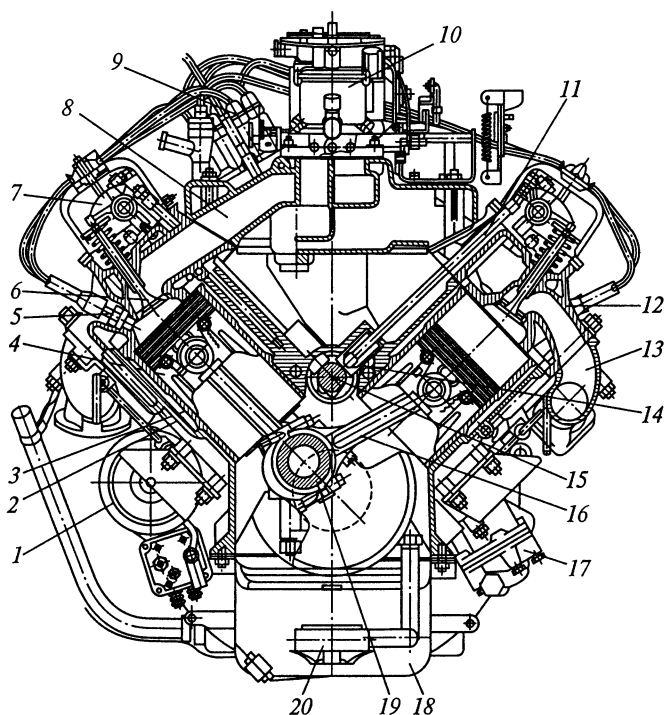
Двигатель легкового автомобиля большого класса:
